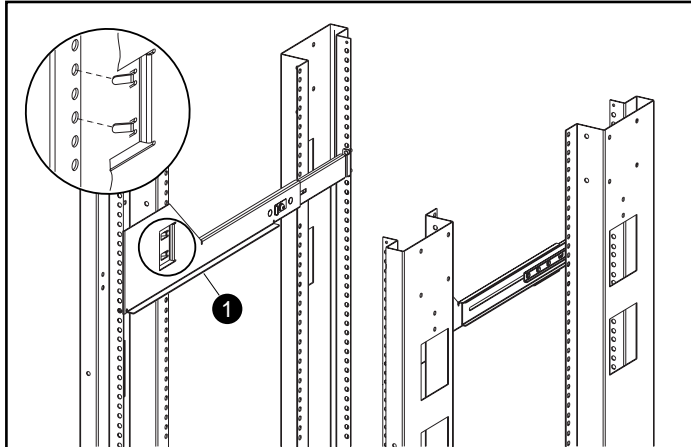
De uitlijningsklemmen bevestigen (alleen voor racks met vierkante gaten)
